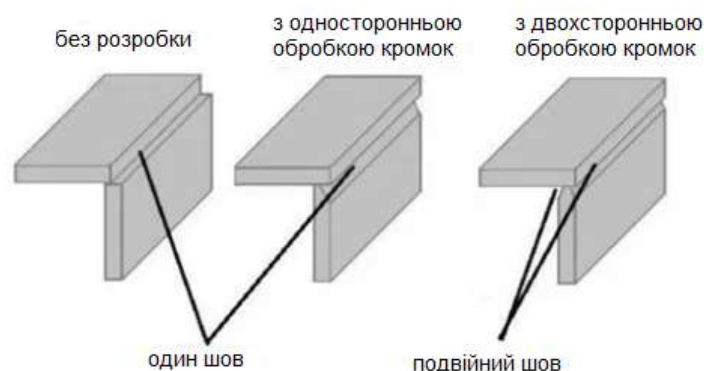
Схема підготовки деталей для утворення кутового з'єднання
